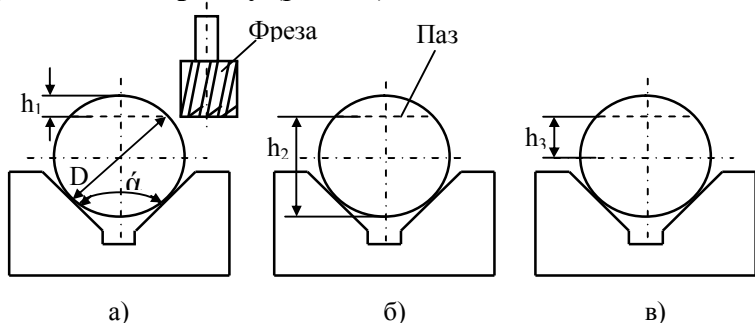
Установка заготовки по наружной цилиндрической поверхности на призму
